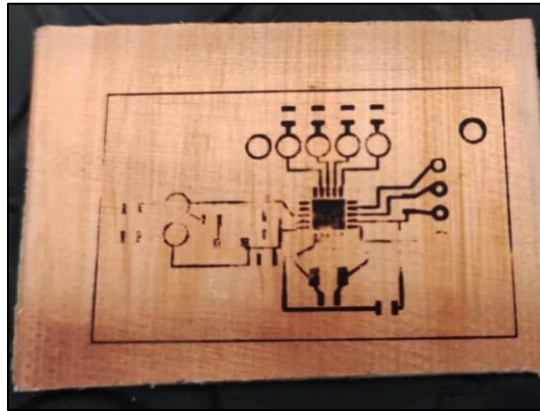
Defectos presentados en la transferencia del diseño al PCB, líneas 0.3 mm.
